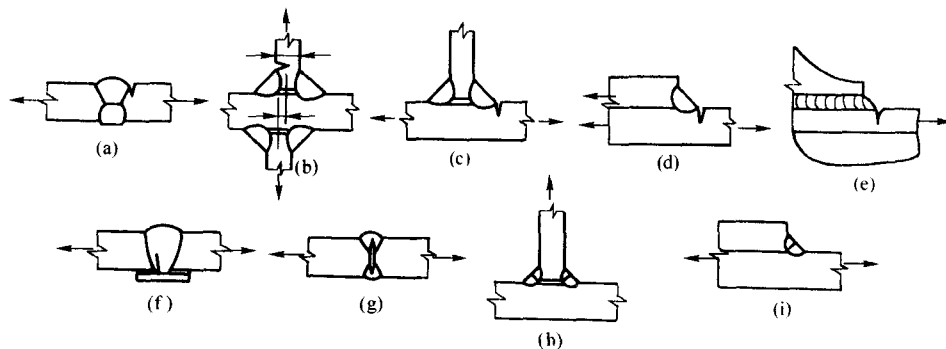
焊接接头不同的裂纹扩展位置
